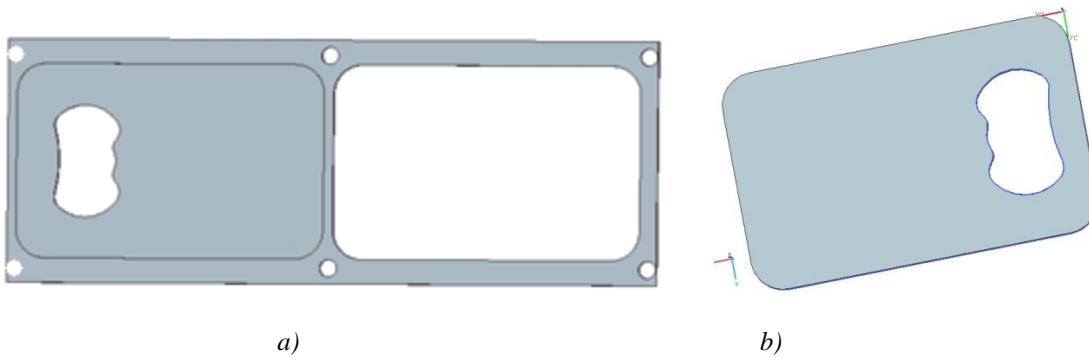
a) Etapa 3. Se perfora la placa para alojar tope del material, se perfora el primer destapador y la cavidad para el segundo b) Tarjeta destapador.
